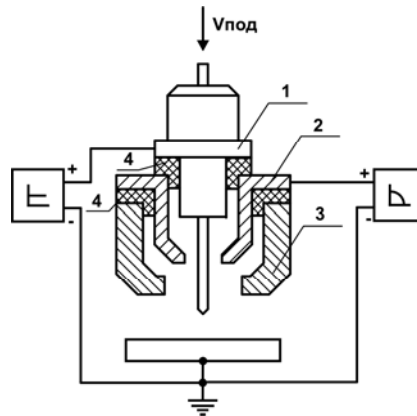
Схема плазматрона для плазменной наплавки комбинированным способом, имеющего кольцевой неплавящийся электрод:
